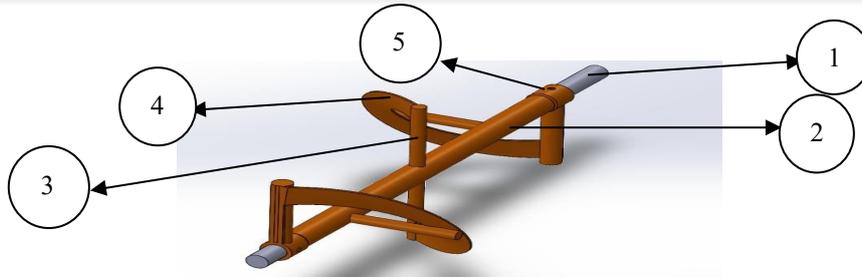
5 Desain Tabung Pada Mesin Pengaduk Pakan Tampak Depan
